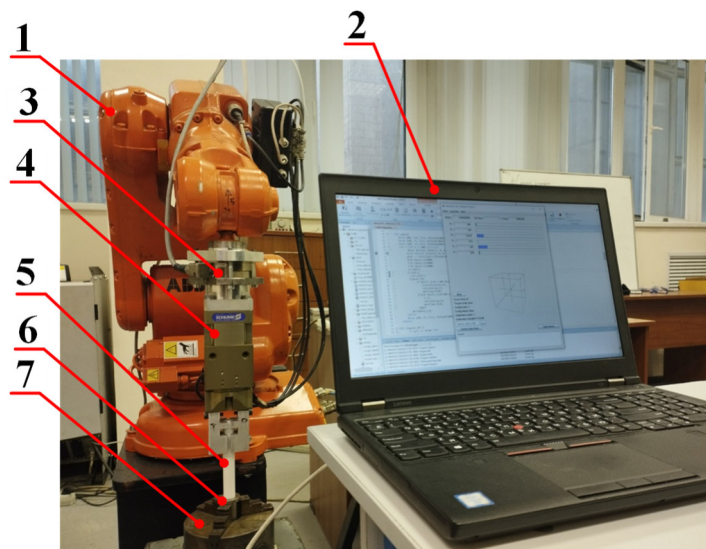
Экспериментальная установка: 1 – промышленный робот АBB IRB 140T; 2 – персональный компьютер; 3 – силомоментный датчик FTN-AXIA 80 SI500-20; 4 – схват Schunk GSM-P 64 E-180; 5 – нежесткий вал; 6 – втулка; 7 – базовое приспособление
